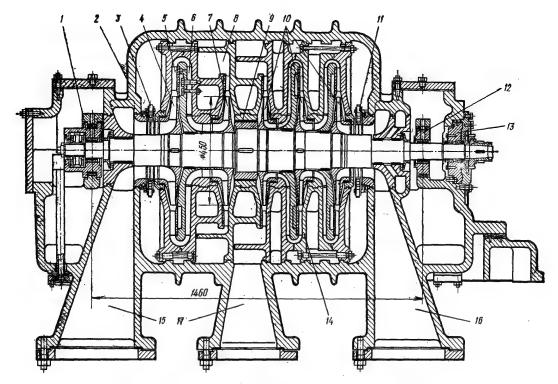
Аммиачный центробежный гомпрессор ТКА-545:
